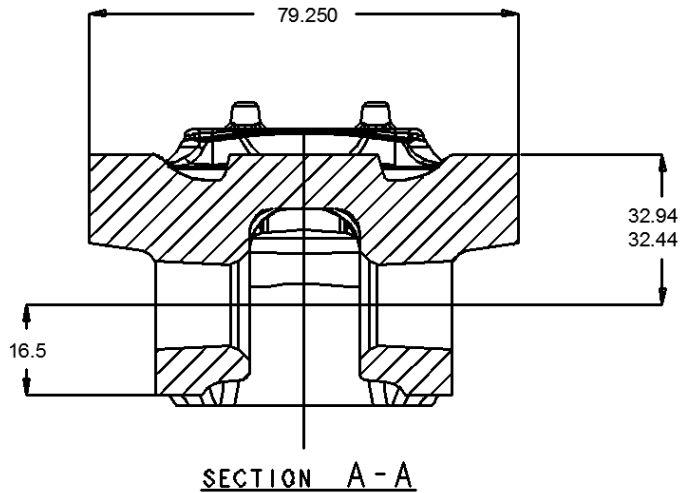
Plano de dimensiones de pistón después del proceso de fundición.
